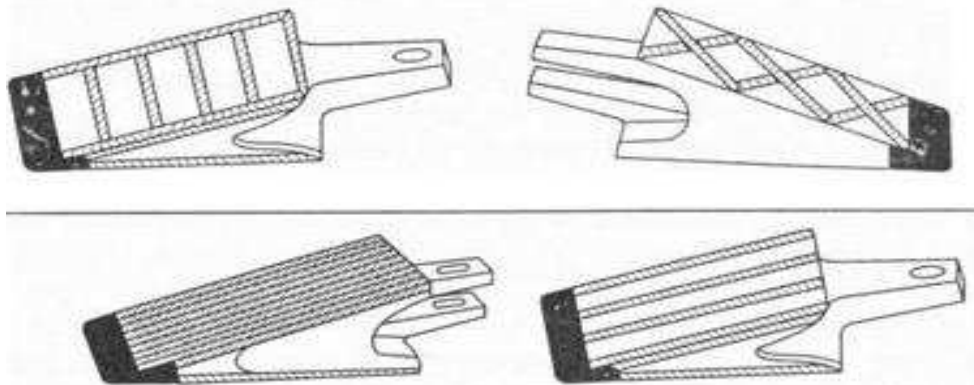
Схема наплавки рабочих поверхностей зубьев ковша экскаватора
